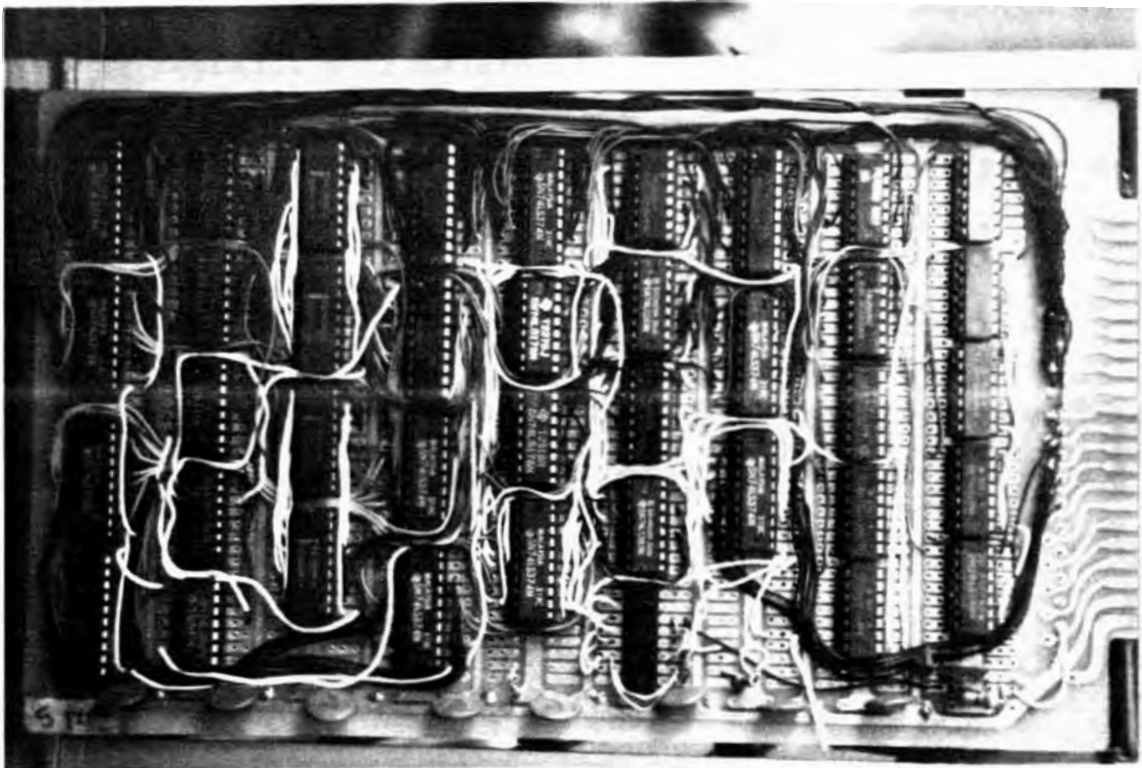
Tarjeta de la etapa de filtro peine.
